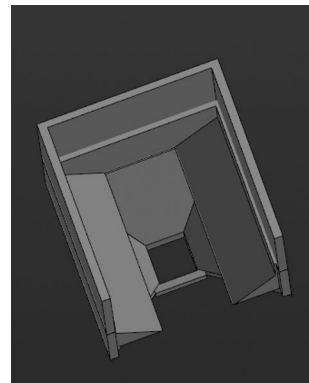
3D-модель мехатронного загрузчика (вид № 2)
